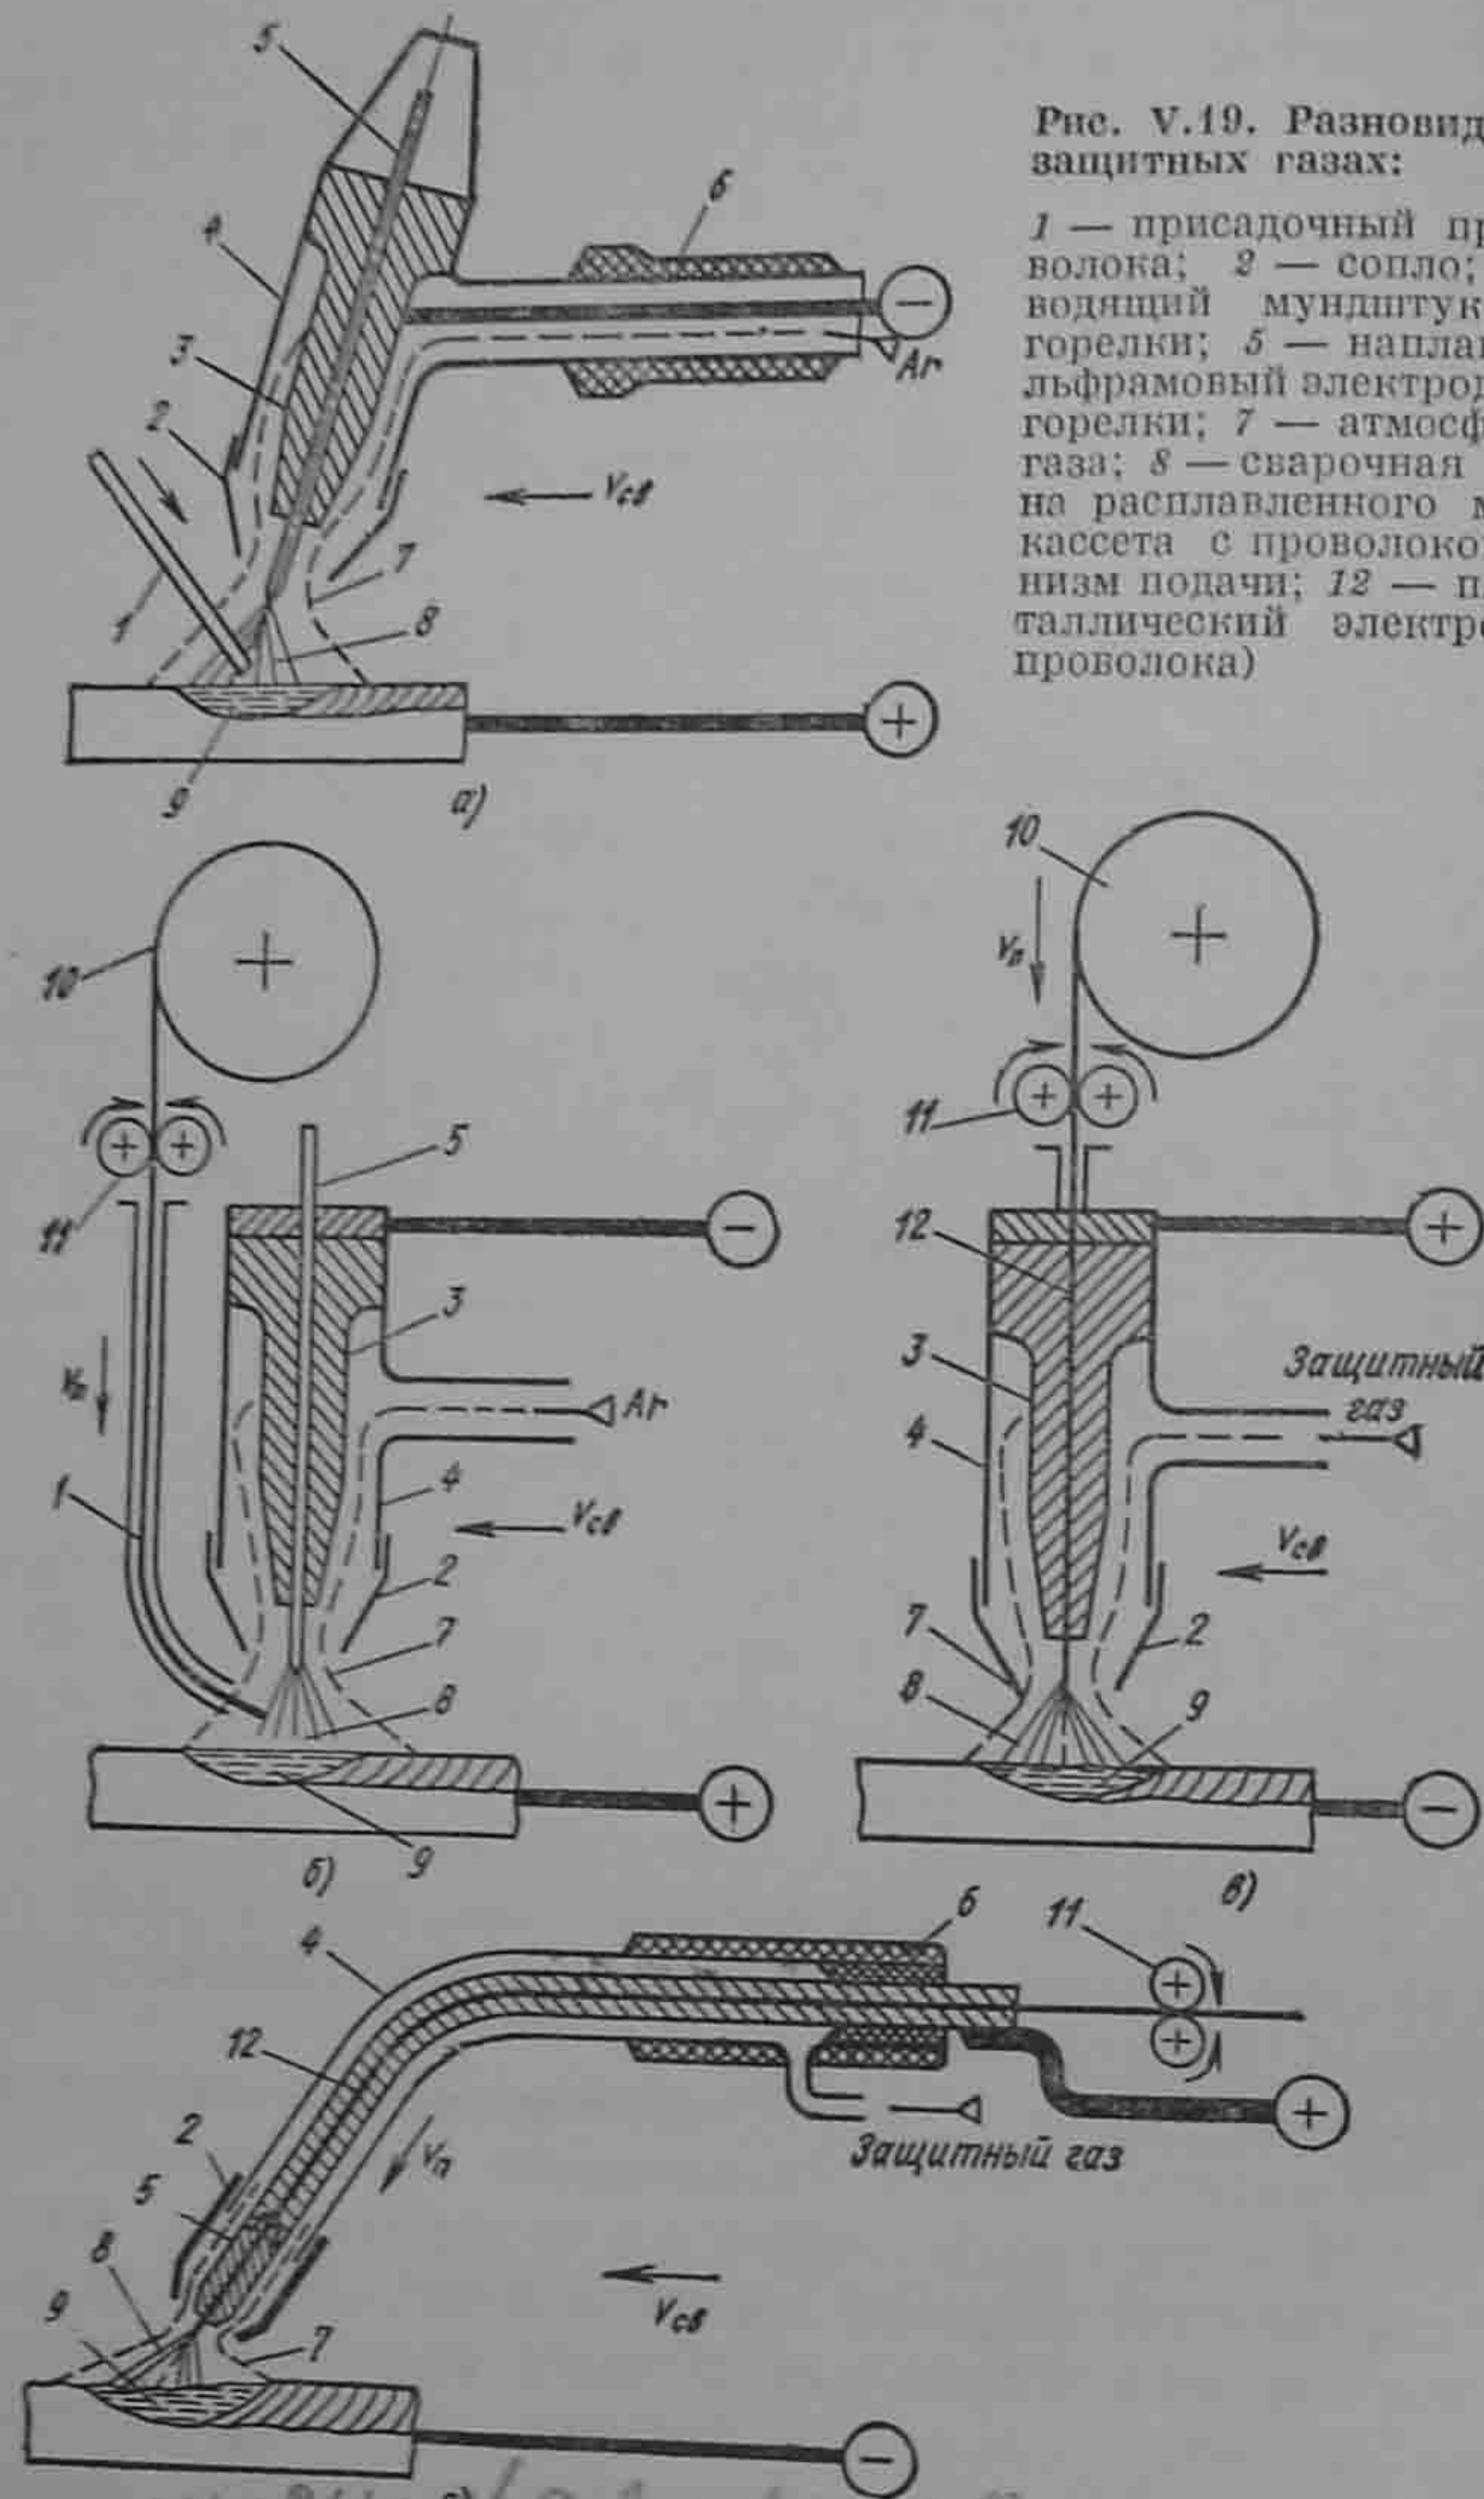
Разновидности сварки в защитных газах:
